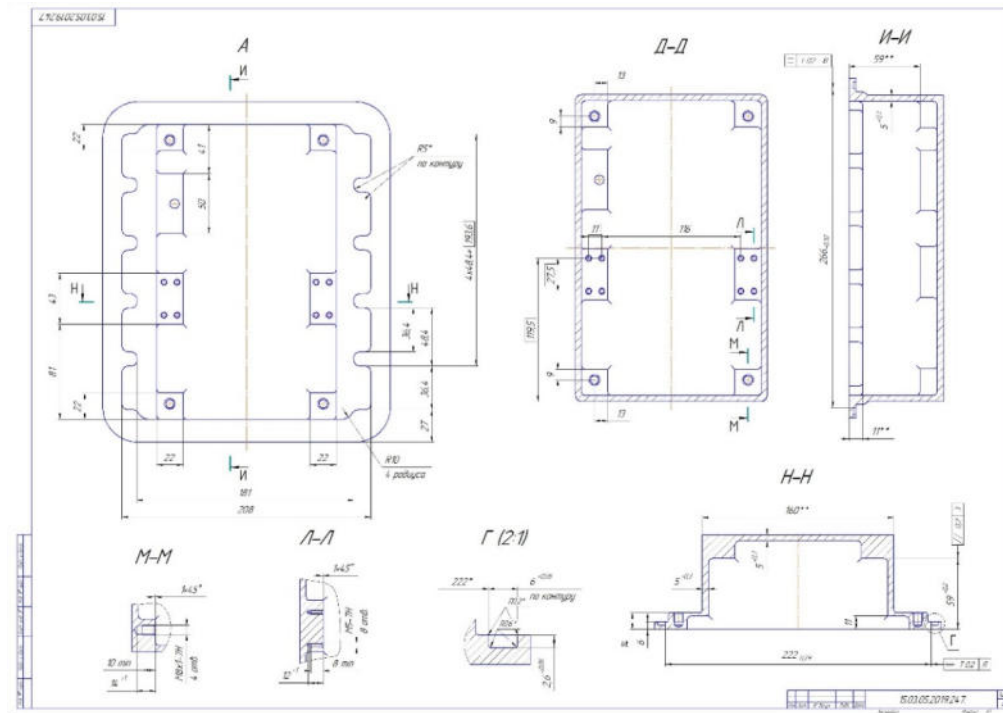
Чертеж детали «крышка задняя» (Продолжение)
